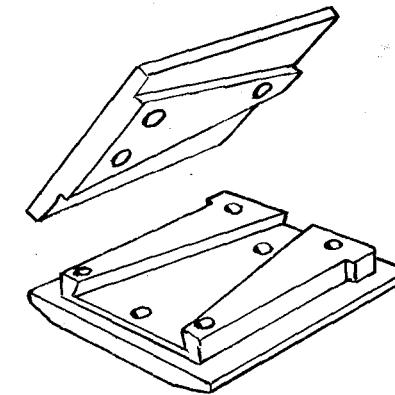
Enganche de ensamblaje para cámaras pesadas.
